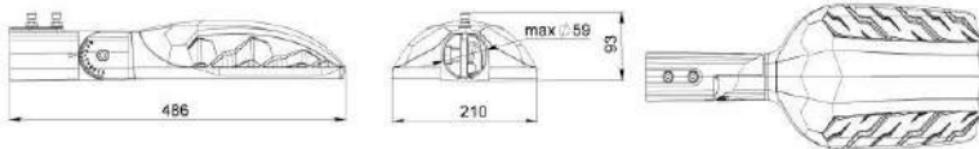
Общий вид светильника Street X1 с консольным поворотным креплением.
